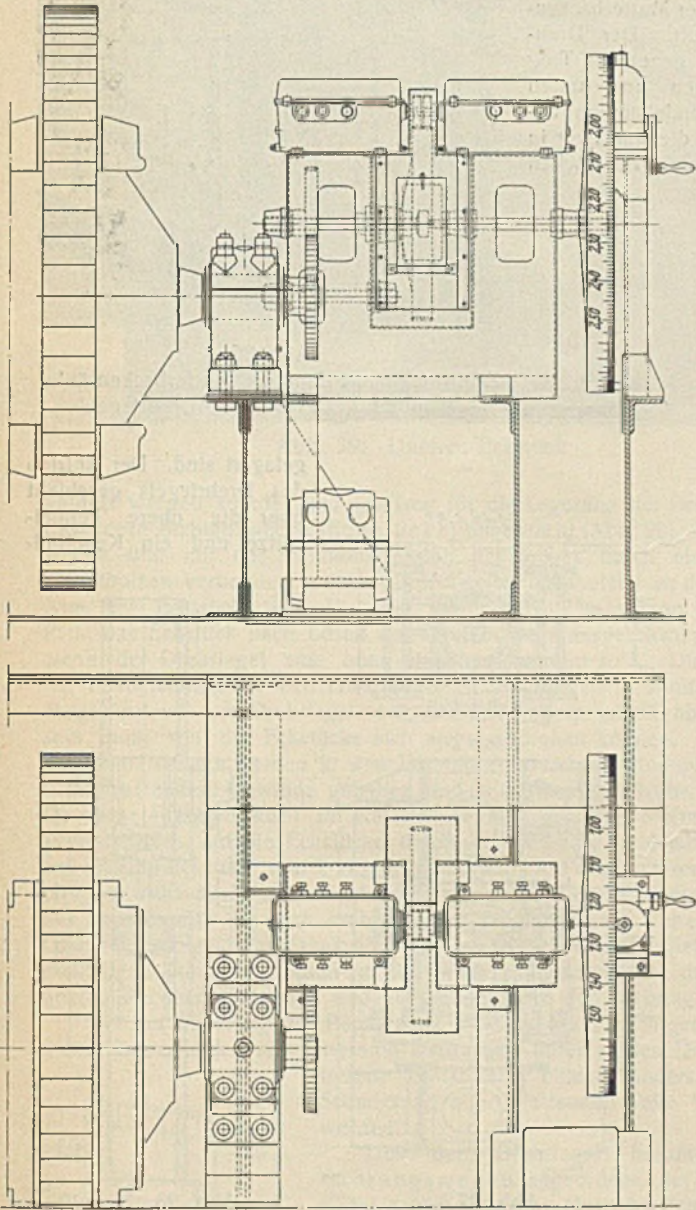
Einstellvorrichtung für die Verzögerungs- und Endausschaltung. Aufriß, Grundriß und Schnitt durch Planetensystem mit Einstellschraube.
